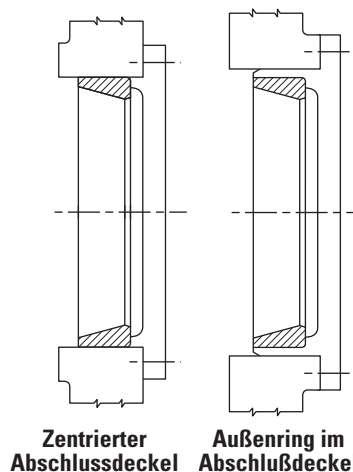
Vorrichtungen zur Lagereinstellung - direkte Montage.
